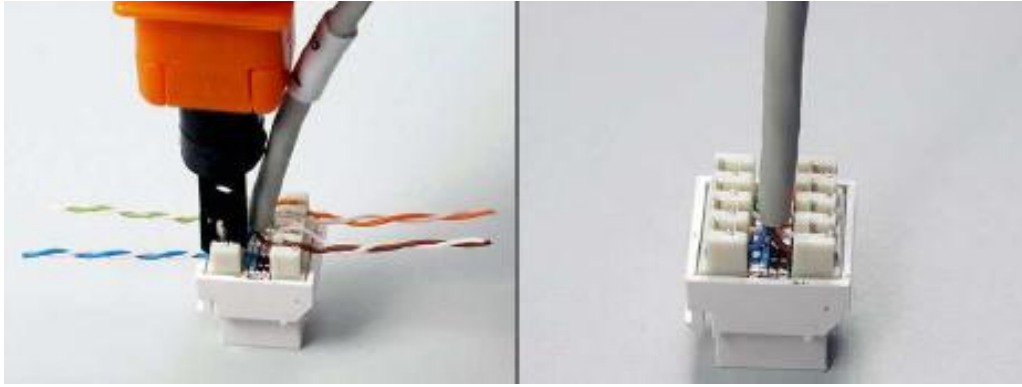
Terminación del ponchado del cable UTP en el jack
